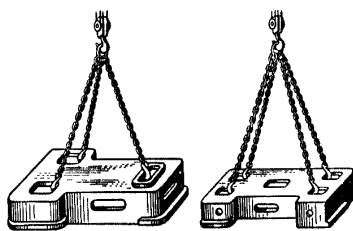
Стropовка отливок за отверстия, расположенные в верхней полости отливок
